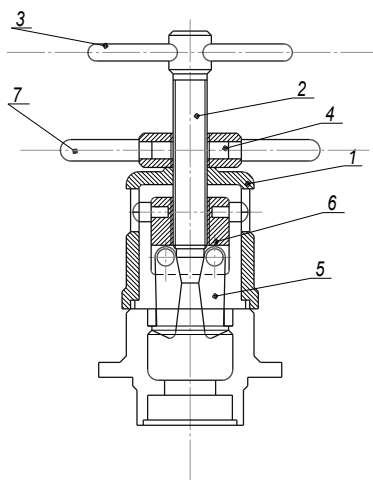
Съемник винтовой для выпрессовки обойм подшипников с помощью захватов
